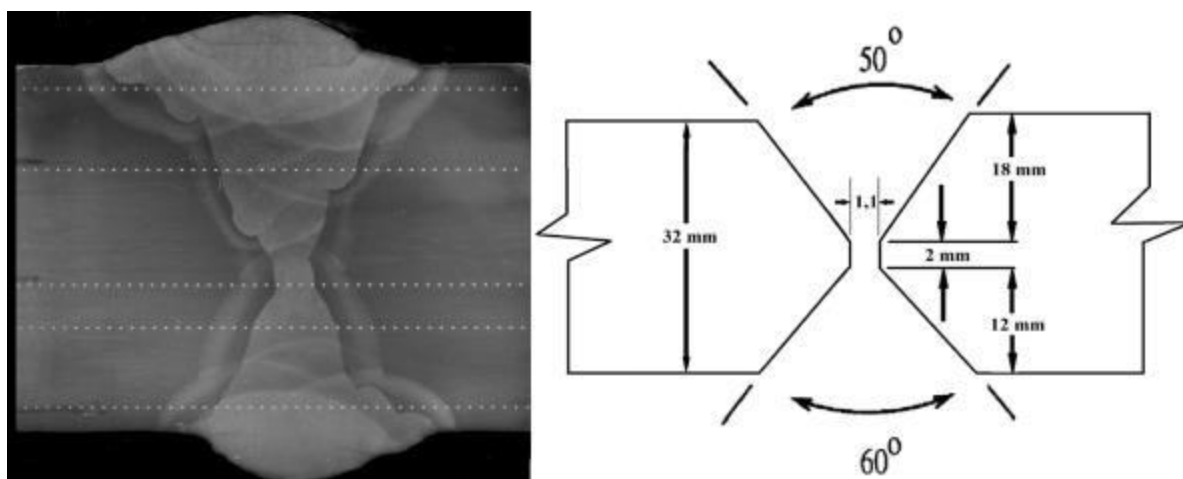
Macrofotografia de uma junta soldada e chanfro utilizado para a soldagem dos segmentos de duto.
